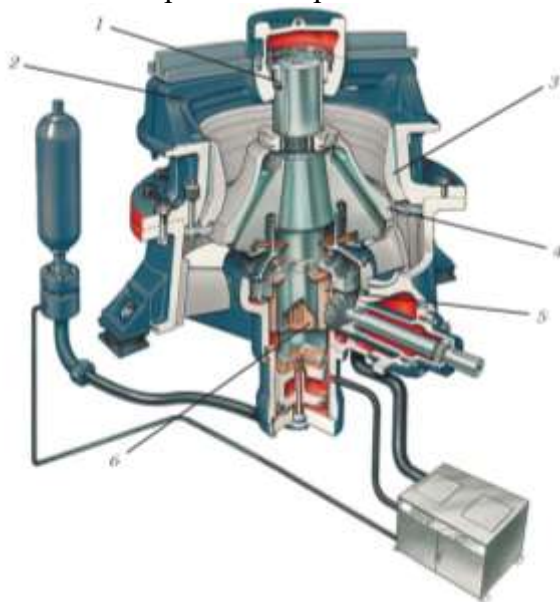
Конусная дробилка SANDVIK: 1 – подшипник траверсы; 2 – верхняя чаша; 3 – футеровочное кольцо; 4 – дробящий конус; 5 – узел эксцентрика; 6 – главный вал.
